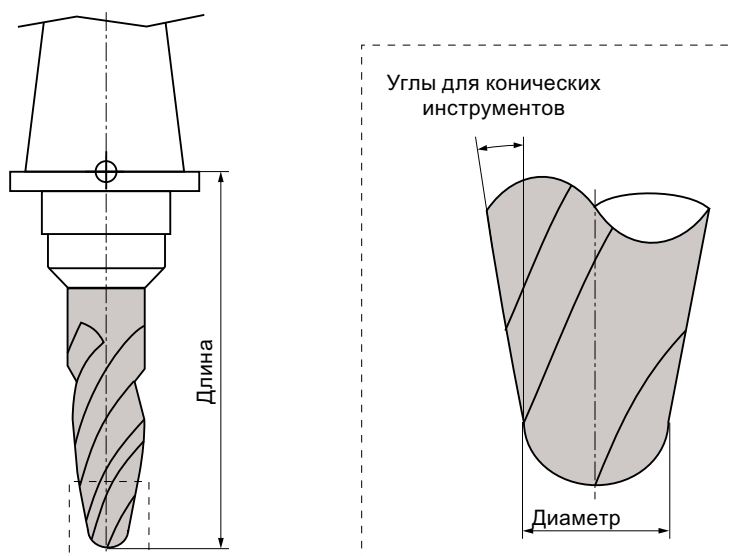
Инструмент 3D на примере конической концевой фрезы (тип 157)
